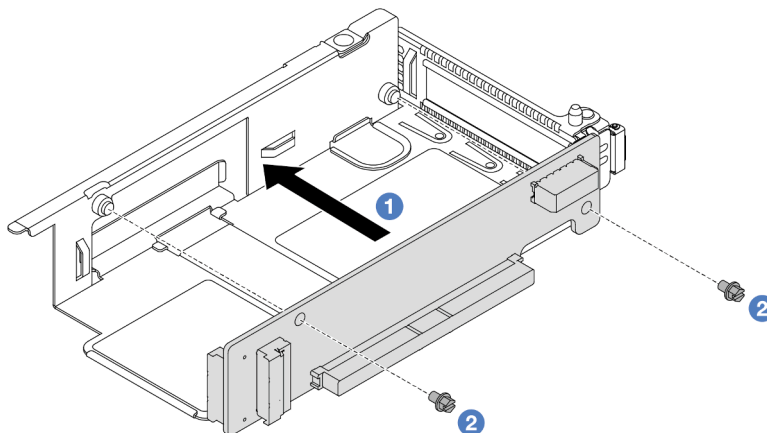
Установка платы-адаптера Riser в низкопрофильный отсек
